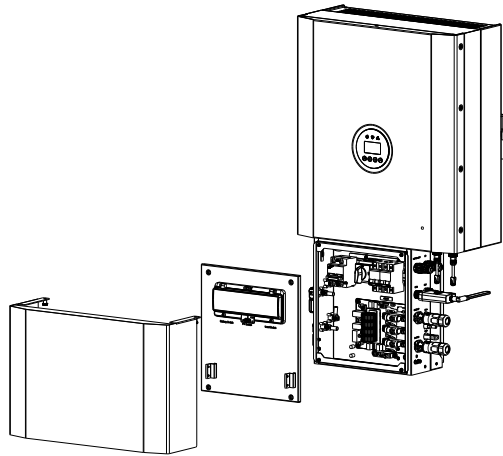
Onduleur sans couvercles de la boîte de câble – Vue de face
